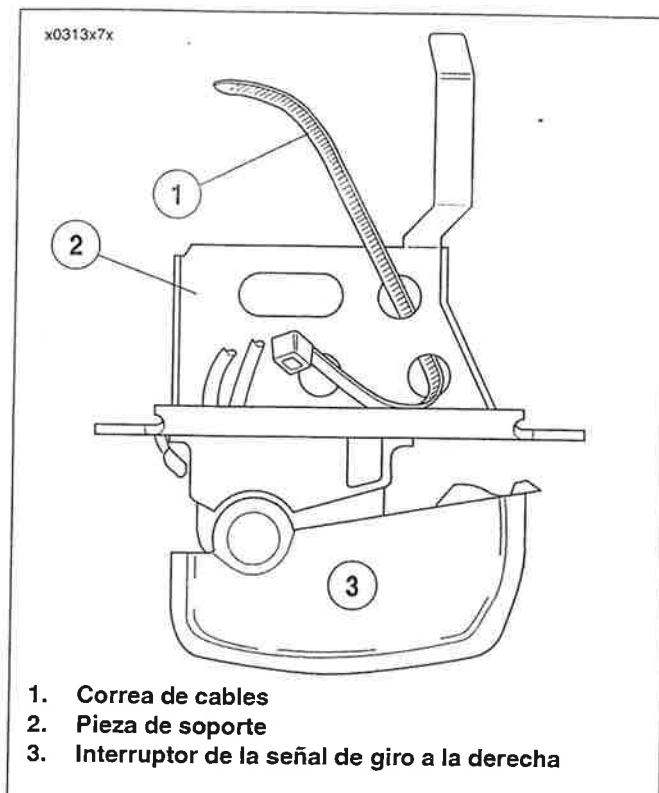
Insertar la correa de cables en la pieza de soporte del interruptor
